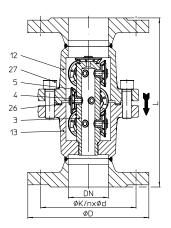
1....10K2 (DN40-50) mit 10 Kapseln, mit Flanschen -Ìn-line-Ausführung
